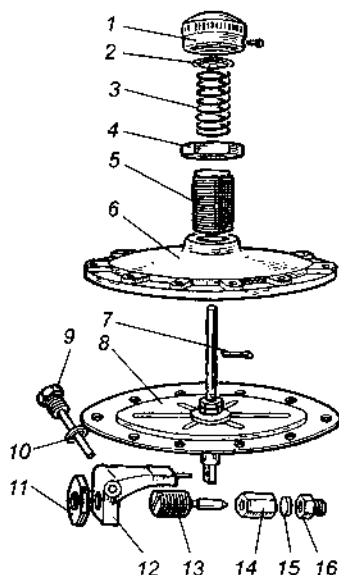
Детали второй ступени редуктора: 1 — колпак; 2 — шайба; 3 — пружина; 4, 11 — контргайки; 5 — седло пружины; 6 — крышка; 7 — шплинт; 8 — мембрана в сборе; 9 — ось рычажка; 10 — прокладка; 12 — рычажок; 13 — регулировочный винт; 14 — клапан; 15, 16 — вставка и седло клапана, соответственно
